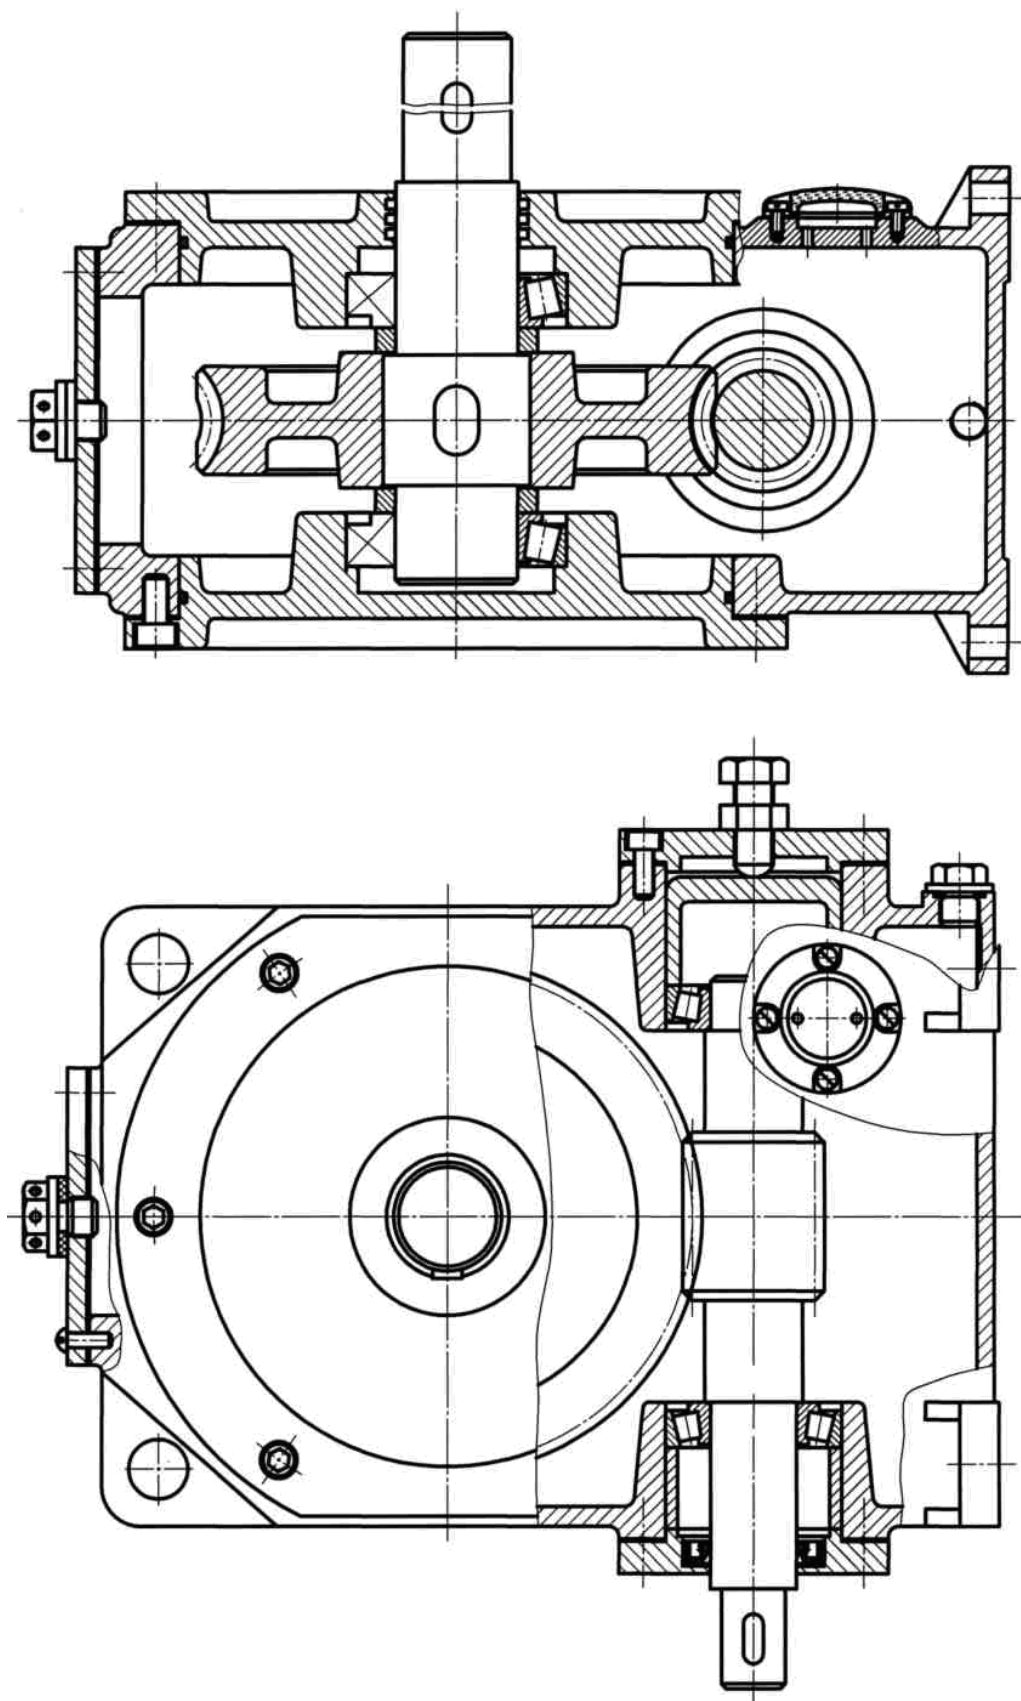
Редуктор червячный с нижним расположением червяка
